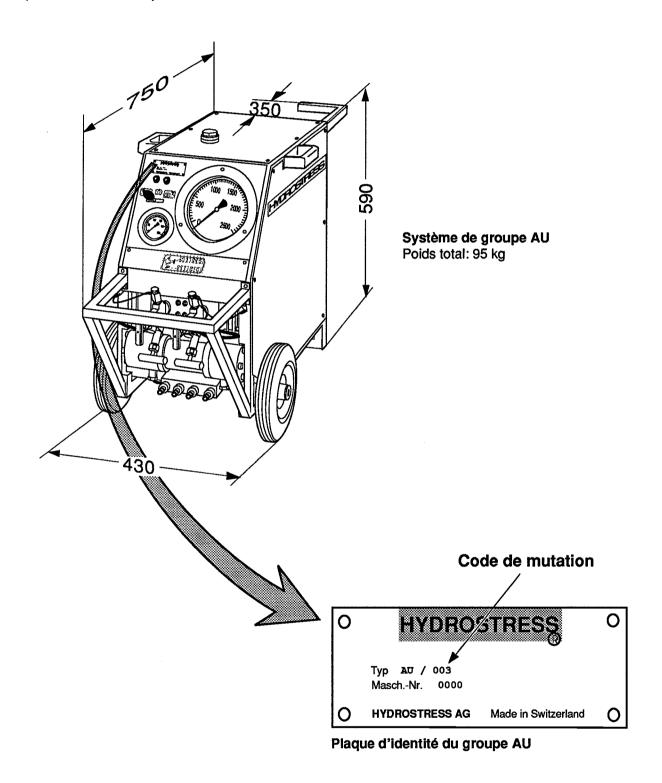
Dimensions, plaque d'identité du groupe AU
